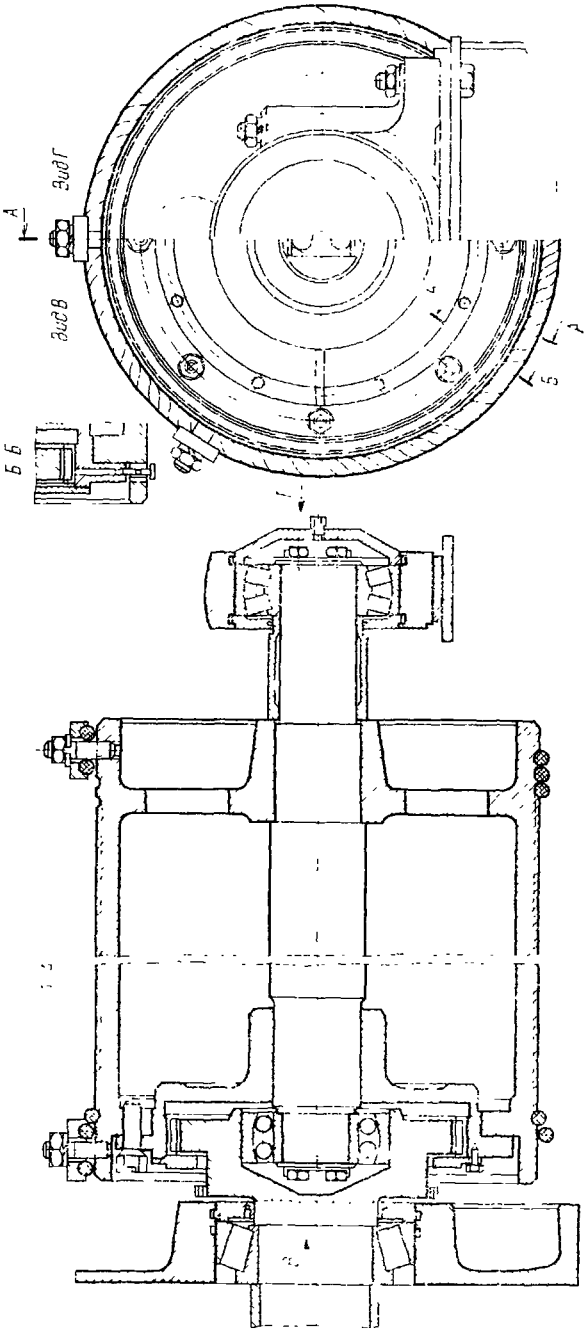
Типовая конструкция соединения барабана с валом редуктора с помощью зубчатой муфты
